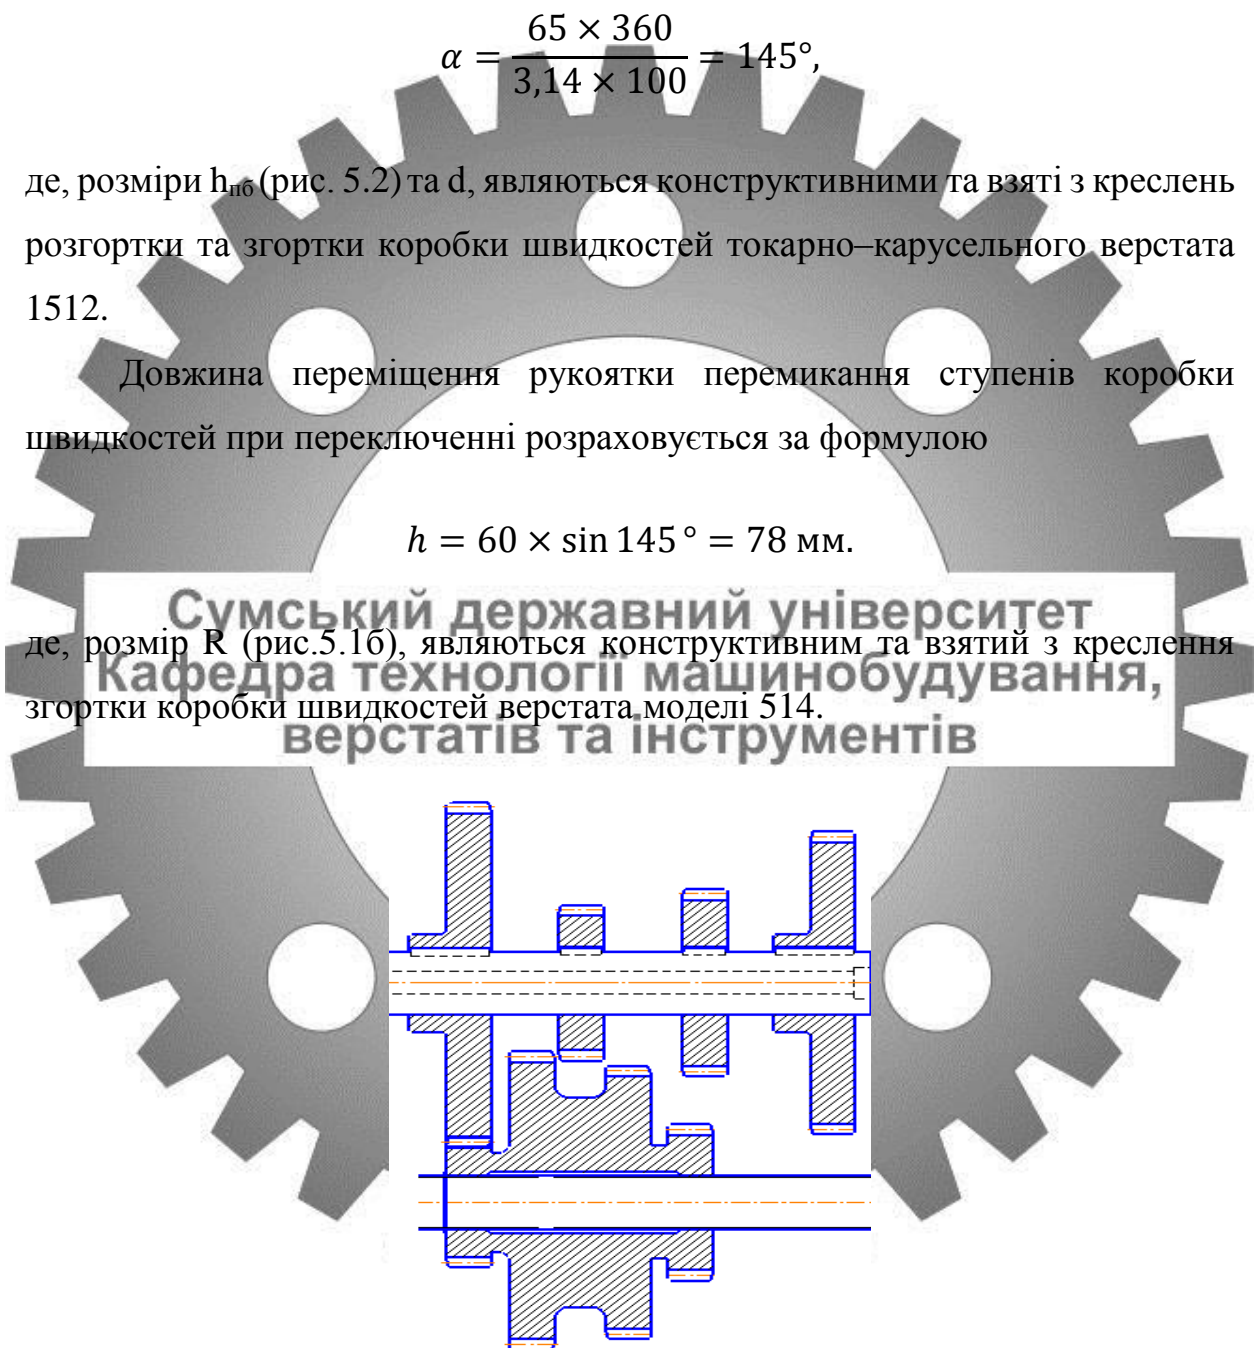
Конструктивна схема переміщення та положення блока зубчатих коліс БЗ– зачеплення Z13/Z107.
